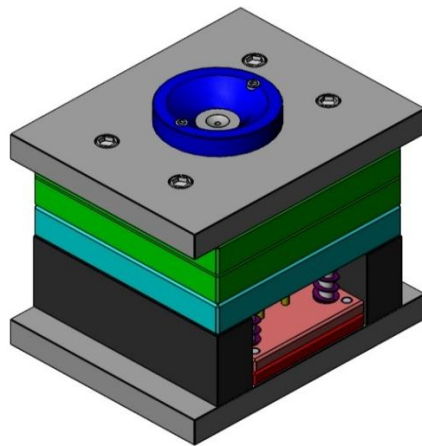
Assembly cavity plate (1) dan core plate (2)
